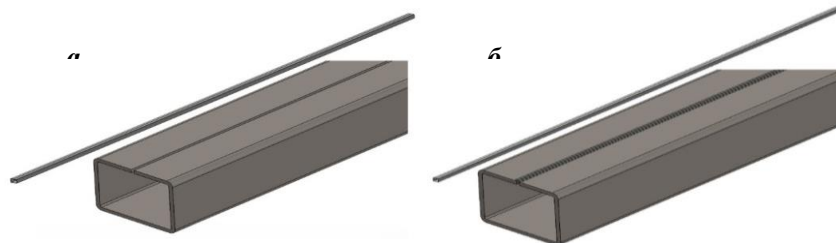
Обв'язування верхнє без зварного шва (а) та із зварним швом (б)
